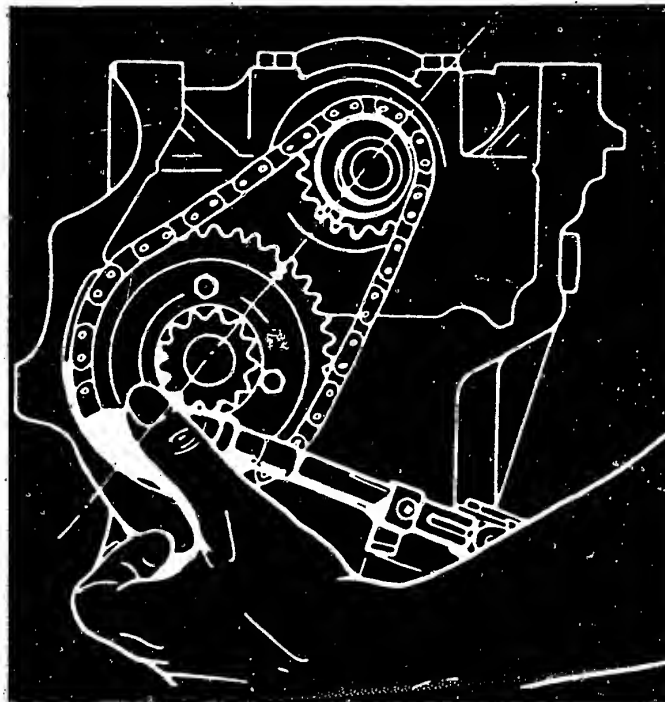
Vor der Montage der Steuerkette sind die Markierungen auf einer Achse auszurichten.
